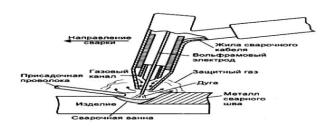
Ручная аргонодуговая сварка нефтепровода БТС 2
